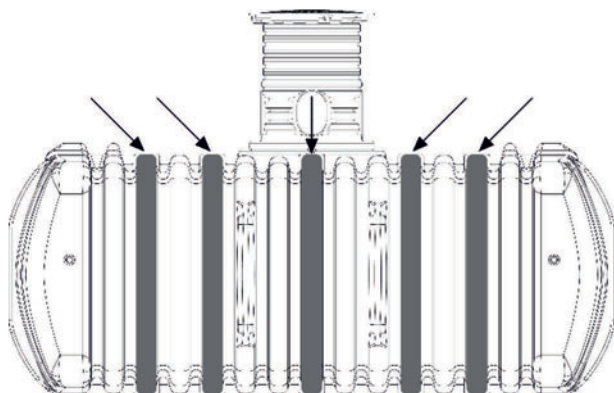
Vue en coupe des tubes de renfort – FLAT XL
